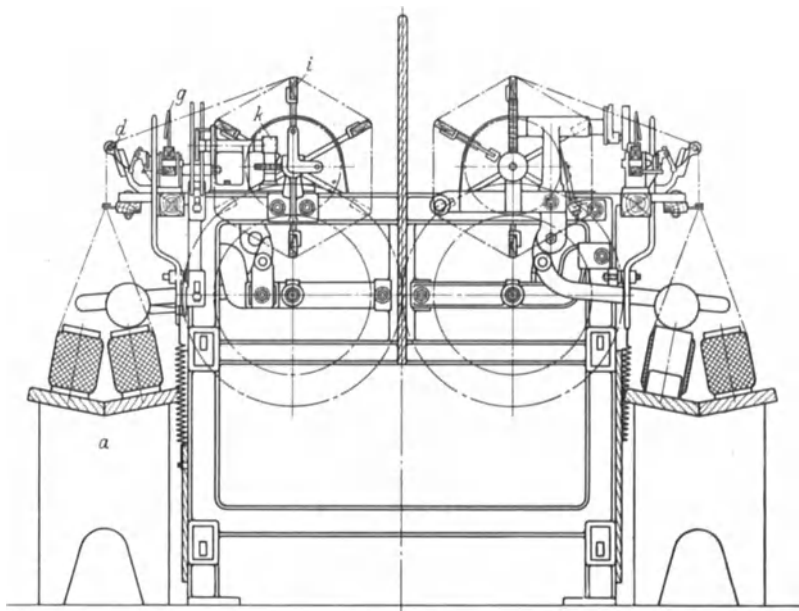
Haspelmaschine. (O. Kohorn & Co., Chemnitz.)
